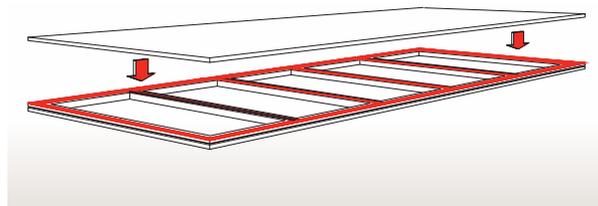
Aplicación de cinta CAP para panel arquitectónico.
